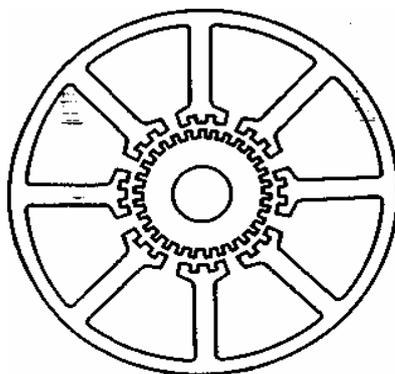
Листы стали статора и ротора шагового двигателя индукторного типа
